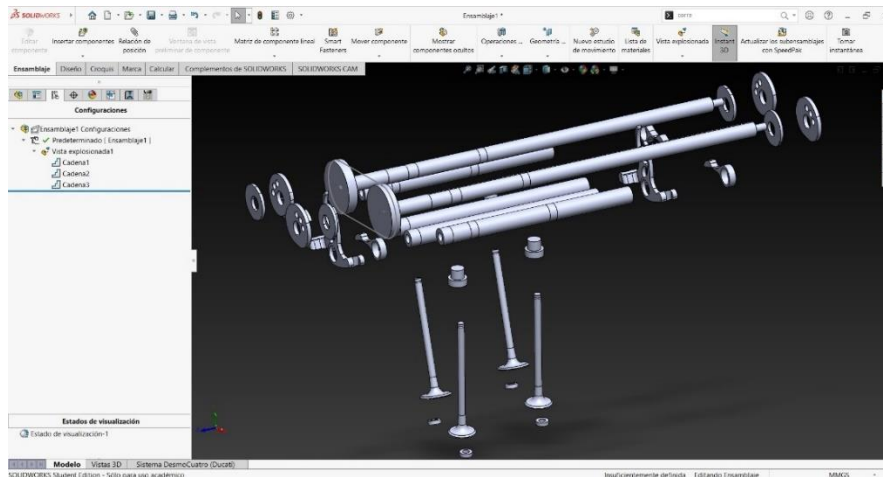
Resultado final del Explosionado. Fuente: SolidWorks
